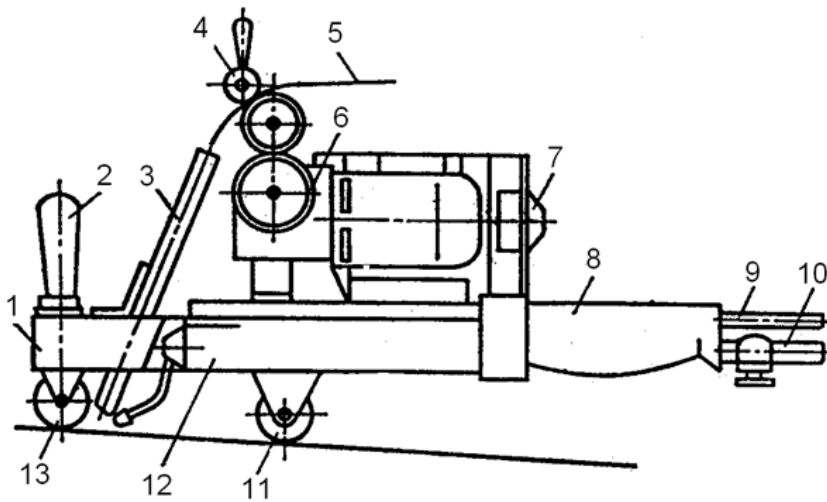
Напівавтомат для зварювання лінолеуму
